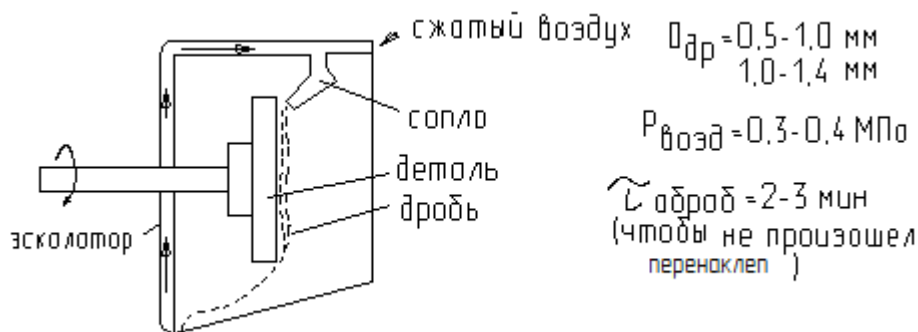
Схема установки для пневмодробеструйной обработки
